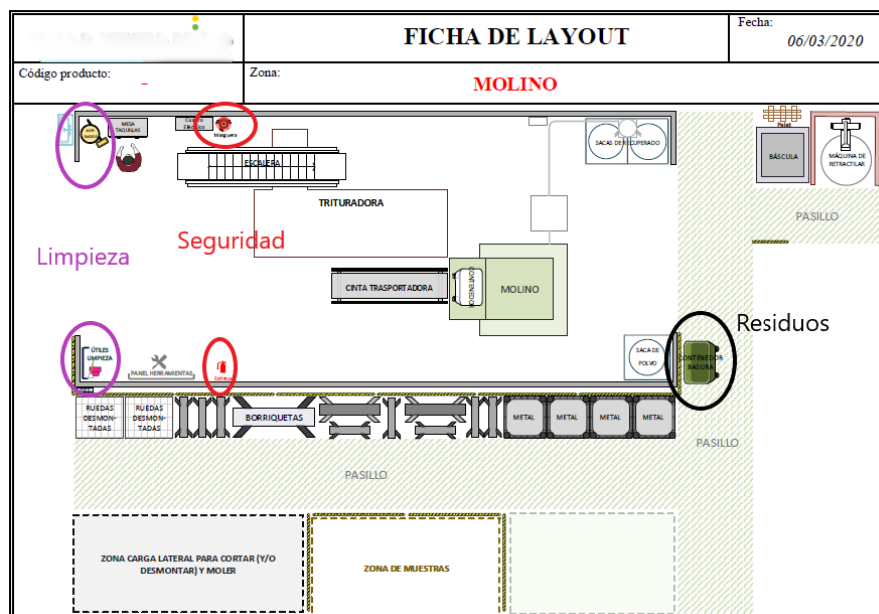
Lay-out de la zona de molino de la planta de Getafe
